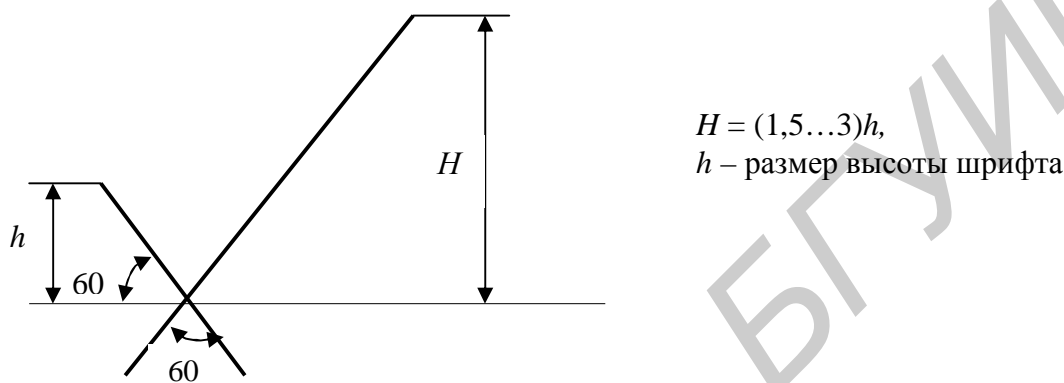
Размеры знака, обозначающего шероховатость поверхности
